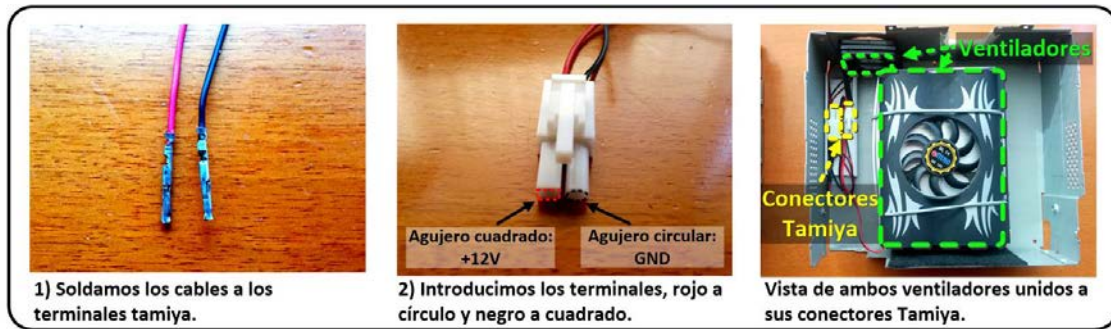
Soldadura de los conectores Tamiya a los ventiladores (Nº Fig. 170).
